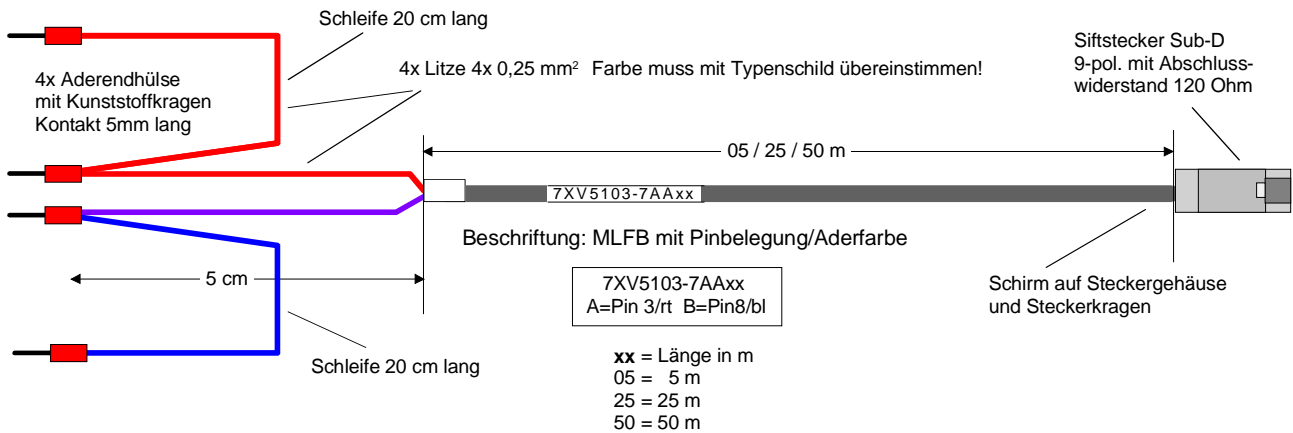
Kabel 7XV5103-7xx für RS485-Bus mit 9-pol. Sub-D Stecker
